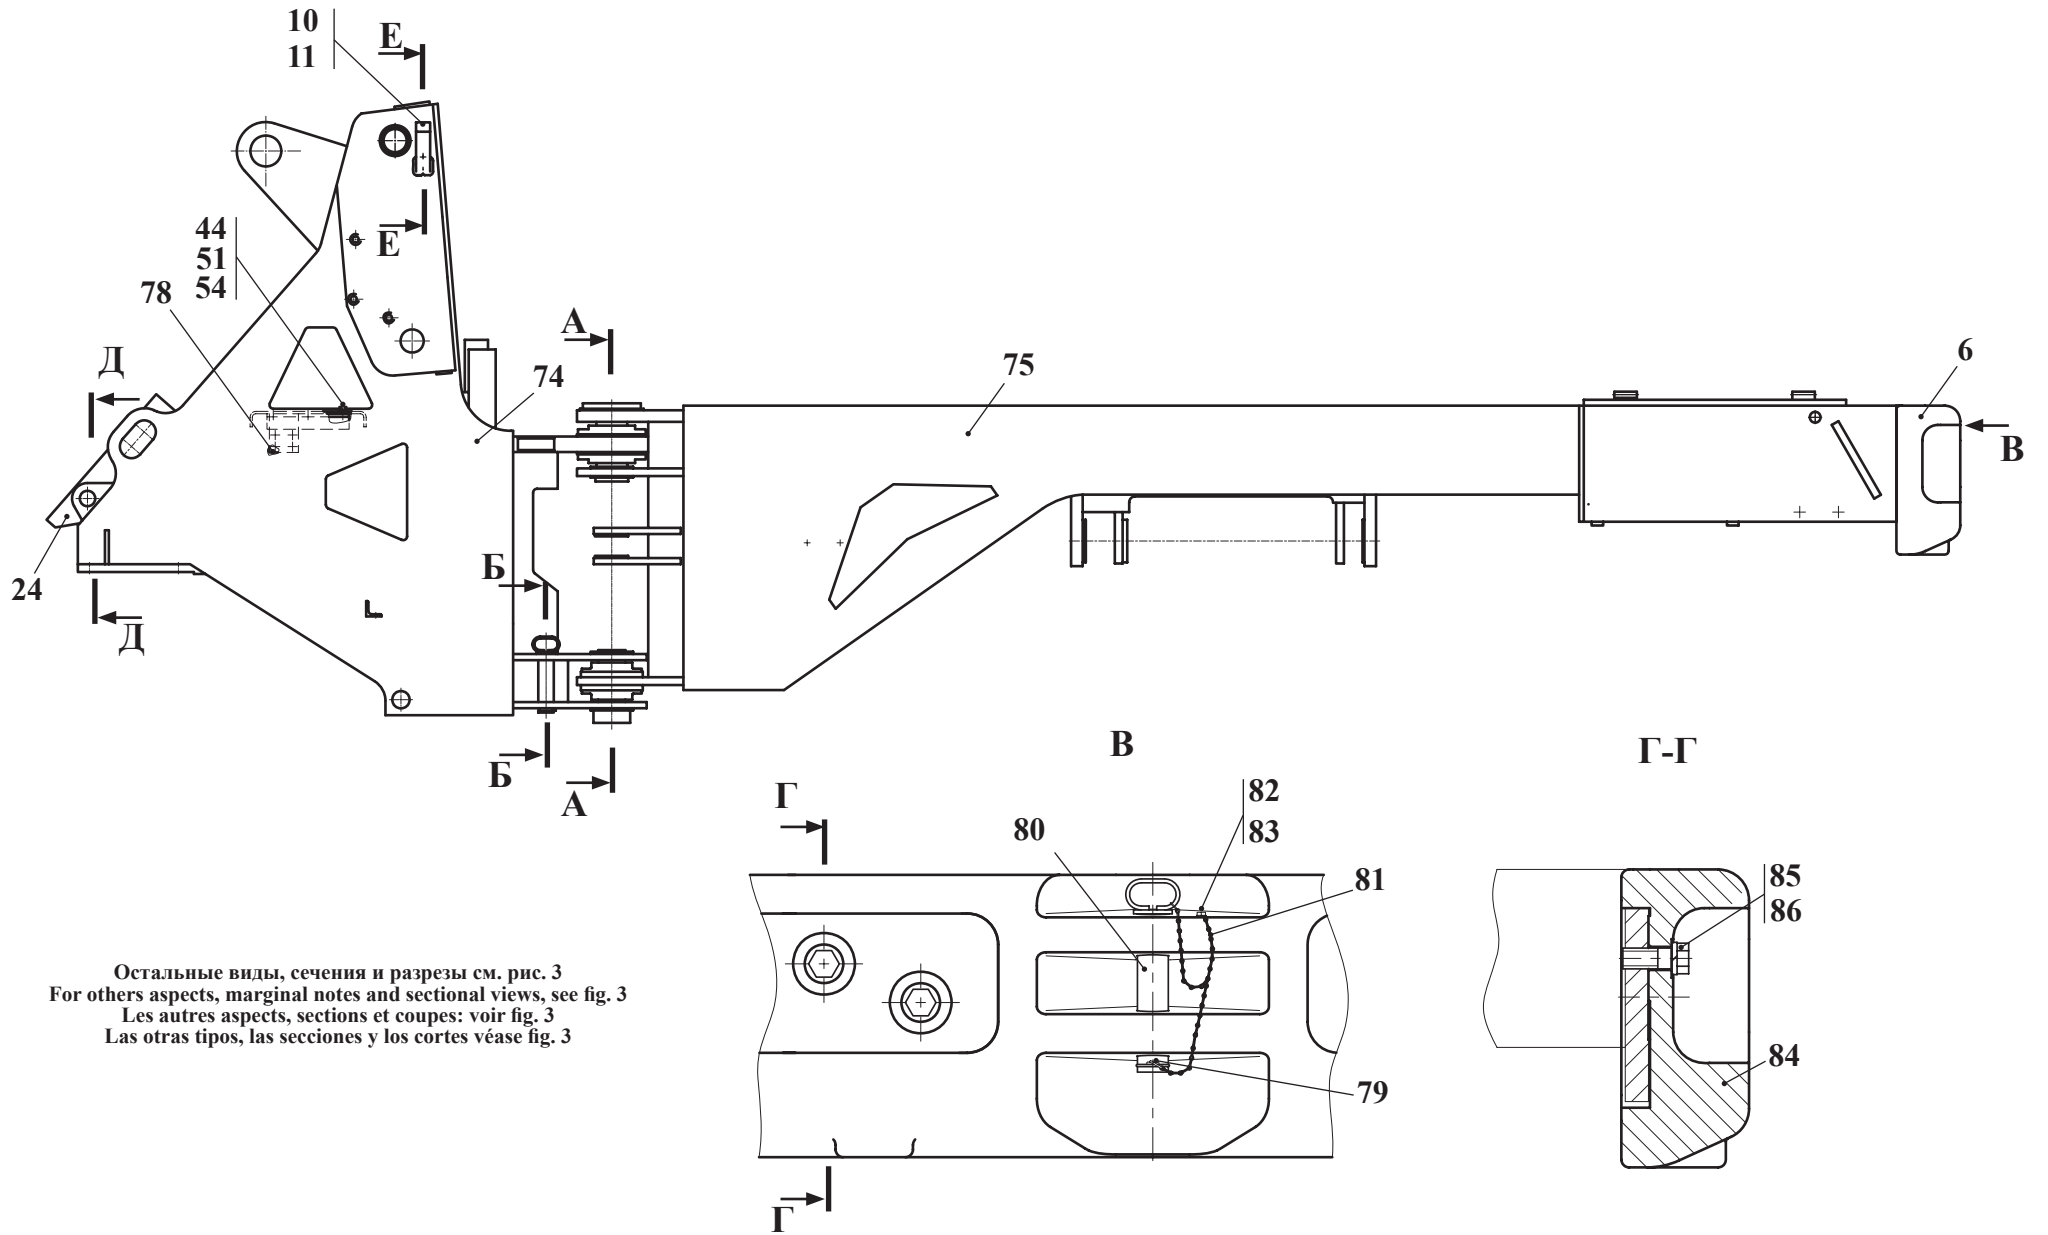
332В.01.00.000	Рама со сварным противовесом
